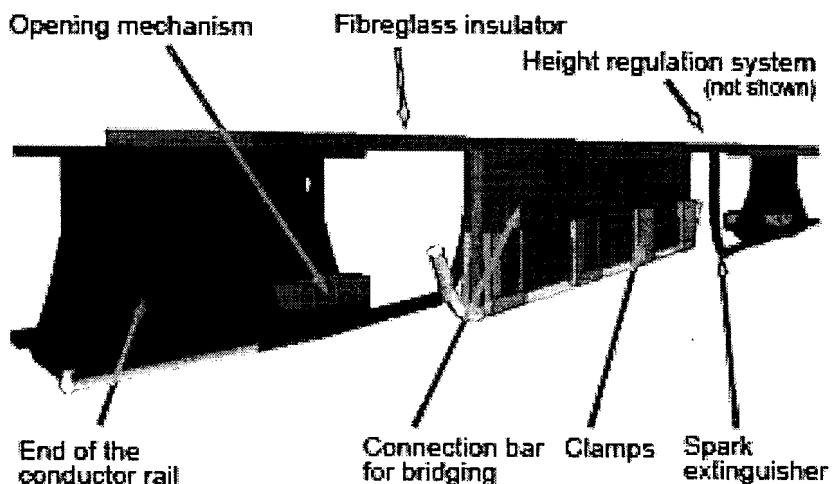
Diseño final del Aislador de Sección METRO_730 (vista elevada y plana)
